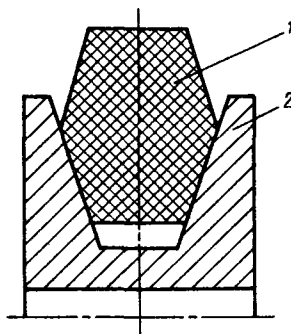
Схема расположения рабочих поверхностей шкива и ремня:
